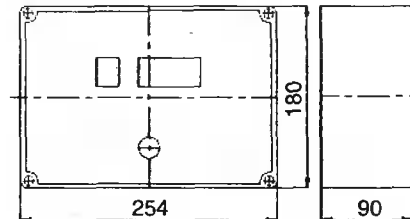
Габариты и внешний вид универсального индикатора в сборе
